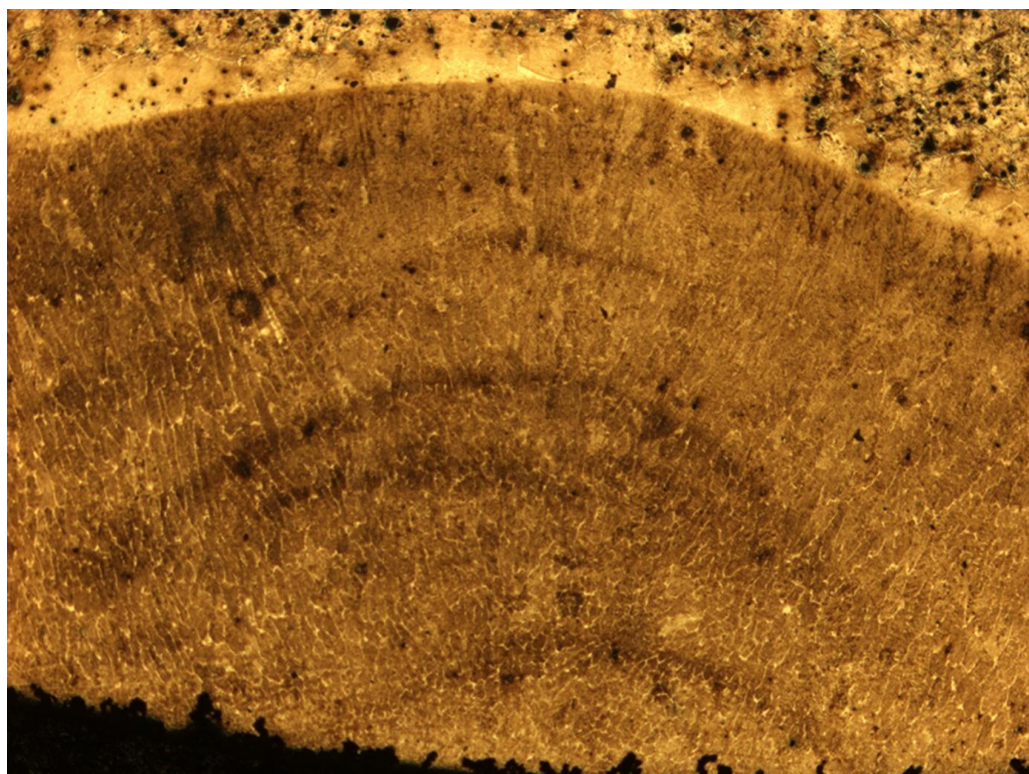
Cordões soldados na fase de testes.
